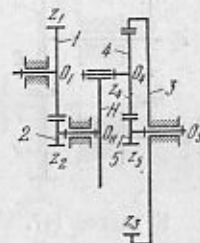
Двухступенчатый редуктор с простой и планетарной ступенями.
